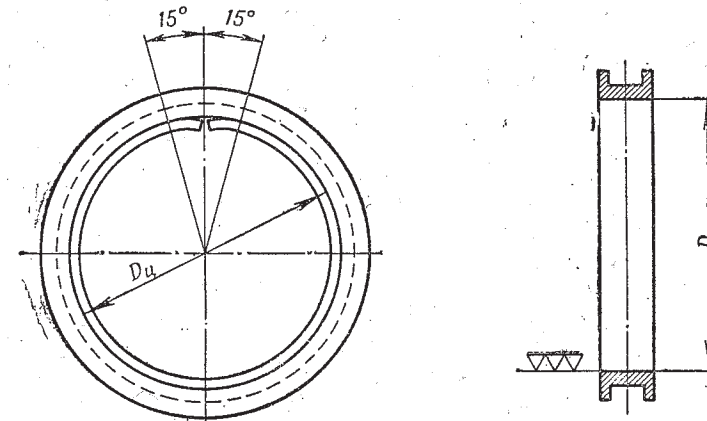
Приспособление для проверки прилегания поршневого кольца:
